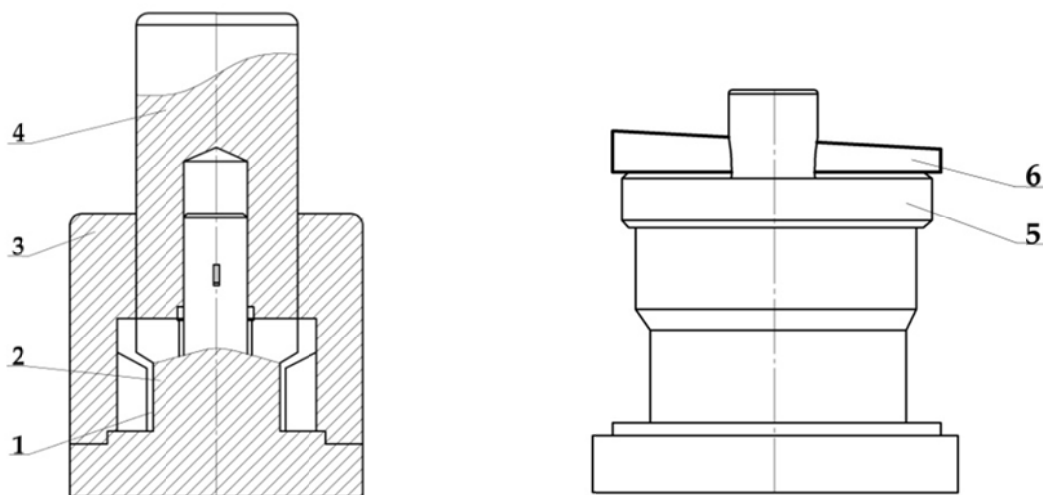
Приспособление для изготовления изоляционных втулок
